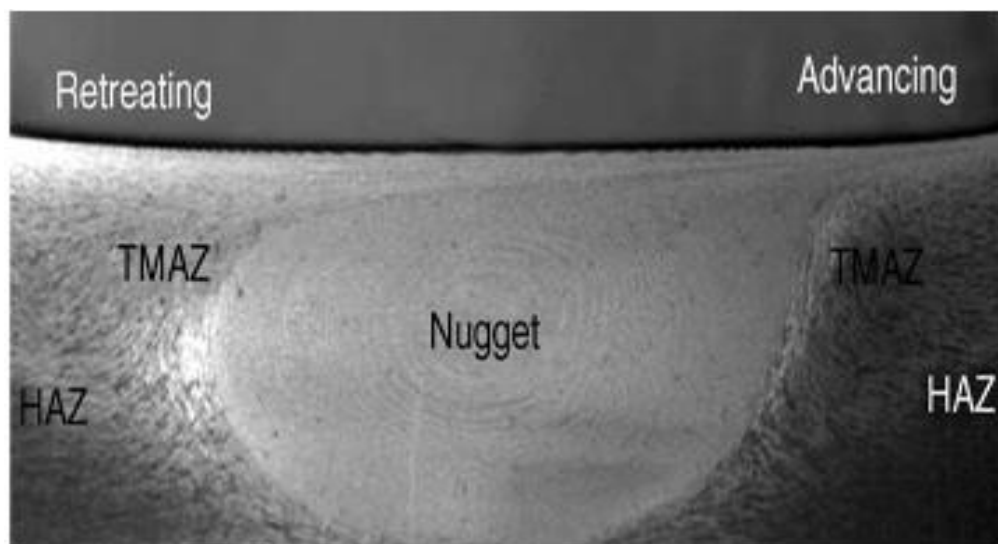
coupe d'une soudure sur un alliage d'aluminium [8]
